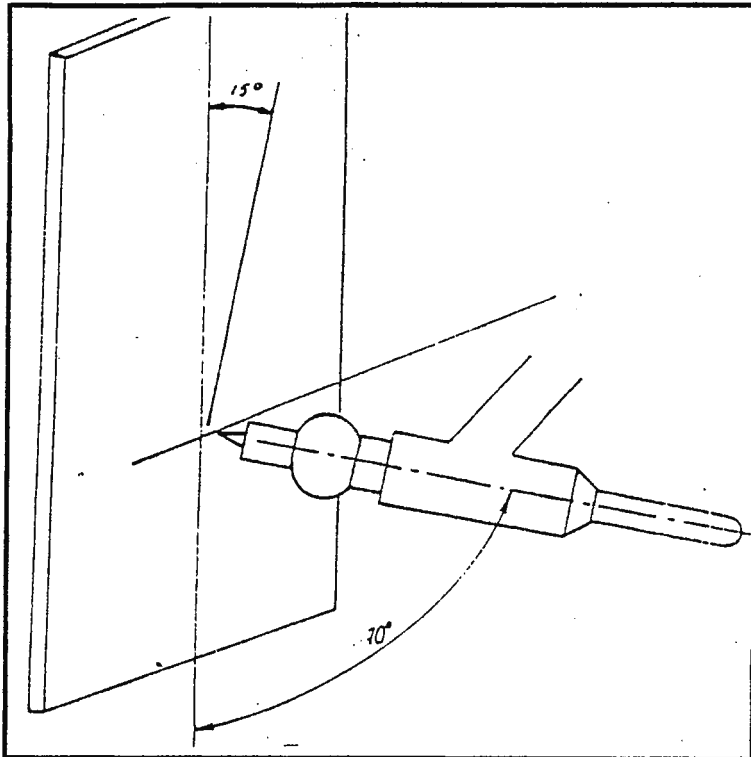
Posición de la pistola los ángulo de este y del metal de aporte en relación con la pistola de soldar
